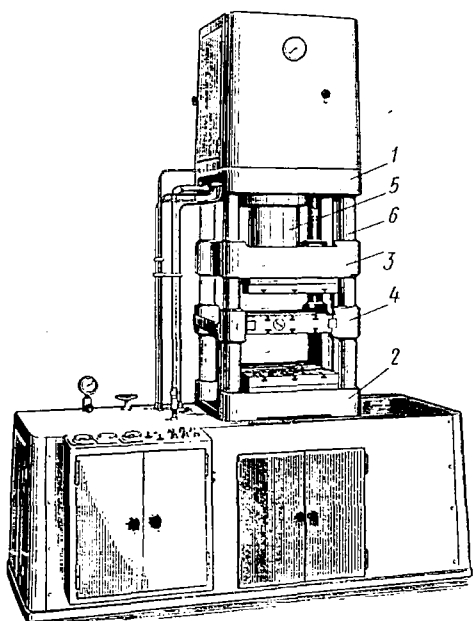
Двухэтажный гидравлический пресс колонной конструкции
